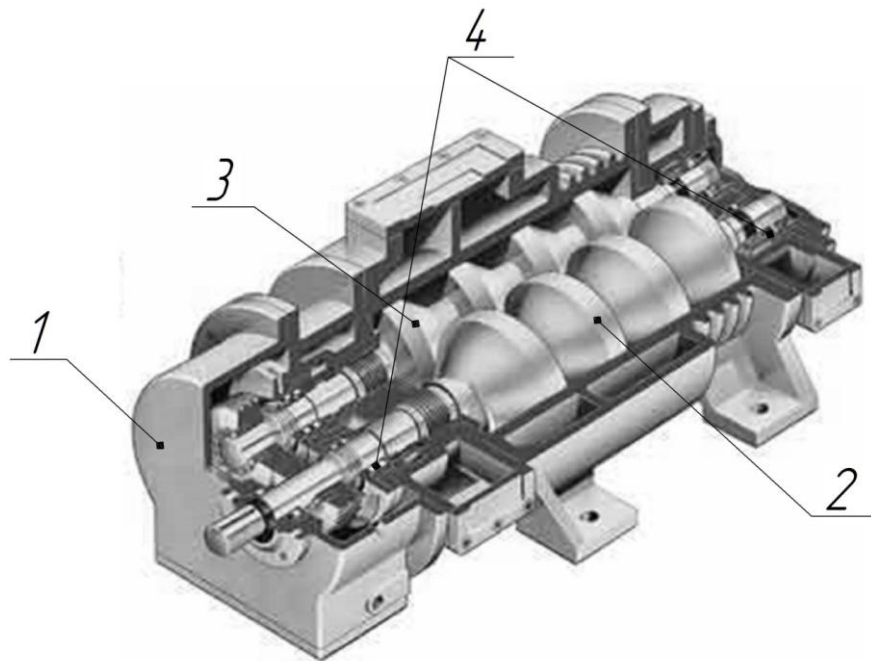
Винтовой насос: 1 - корпус, 2 - ведущий вал, 3 - ведомый вал, 4 – підшипники
